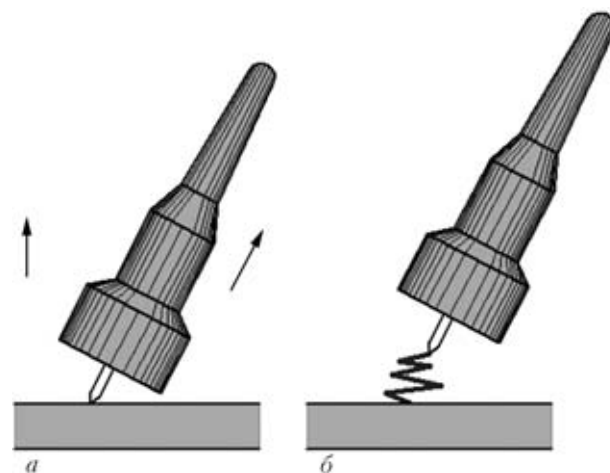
Схема поджига дуги при ручной сварке ТИГ титана с использованием горелки с «газовой линзой» касанием (а) и с помощью осциллятора — устройства стабилизации горения дуги (б)
